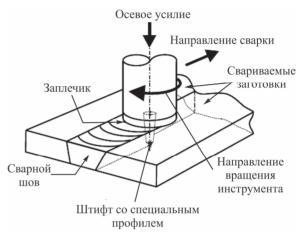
Процесс сварки трением с перемешиванием
